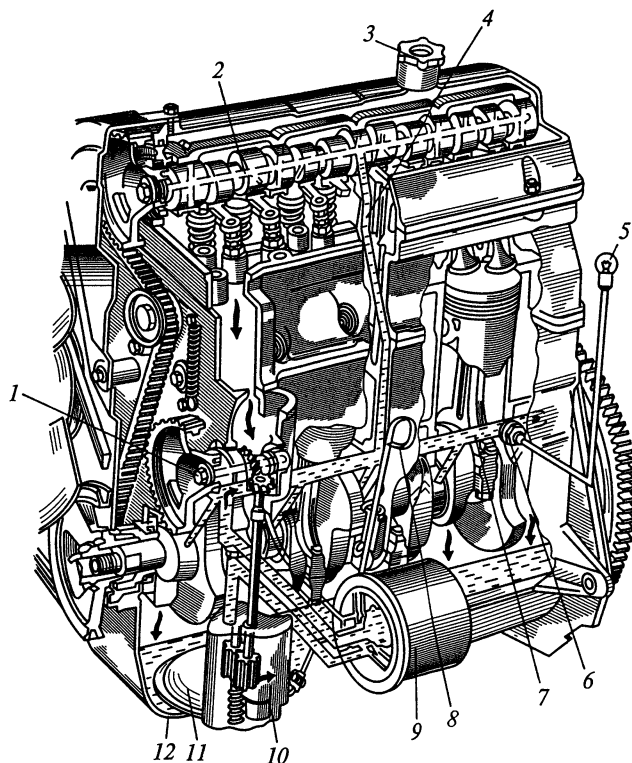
Смазочная система двигателя легкового автомобиля:
